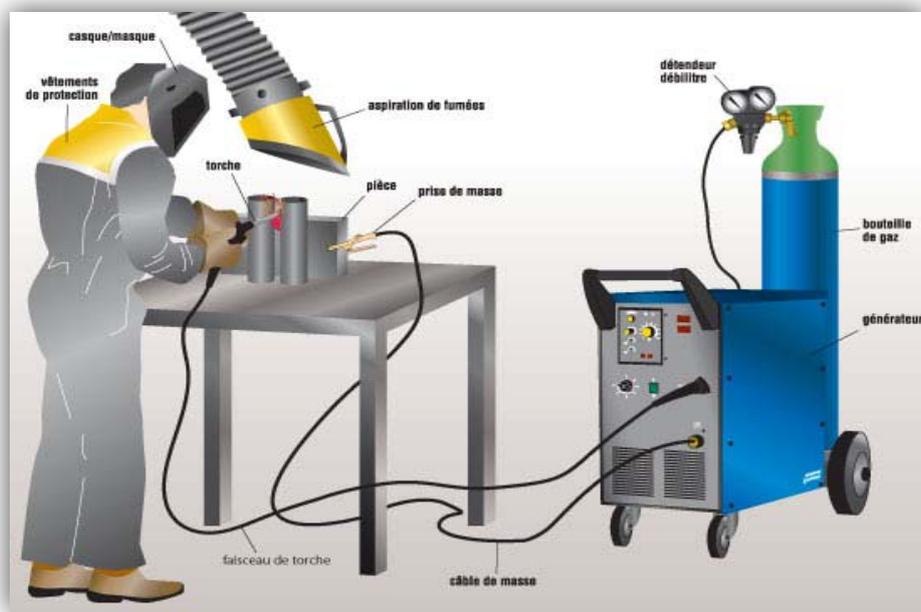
Le soudage à l'arc électrique type TIG.
